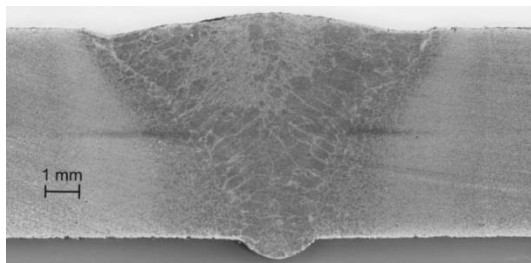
Soldagem realizada com o processo TIG utilizando a técnica *keyhole* em chapa de aço com 6,35 mm de espessura [2]
